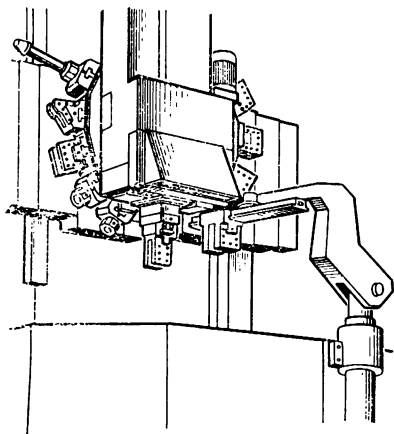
Инструментальный магазин станков серии SKQ NC завода TOS
